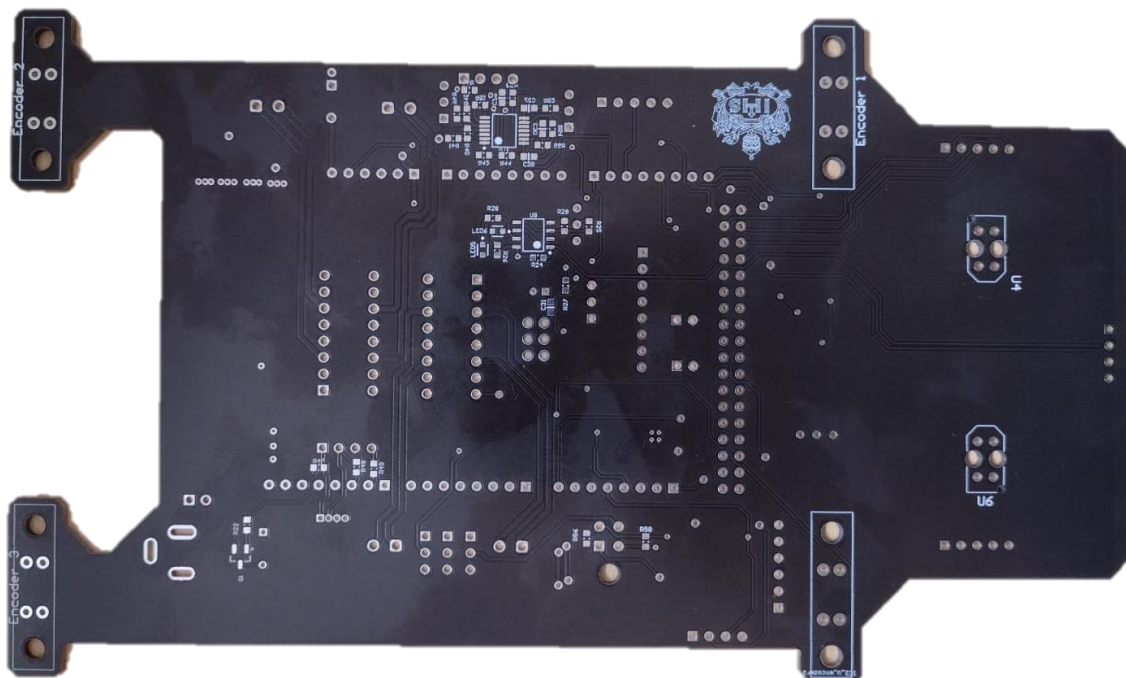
Vista inferior del PCB fabricado versión 3 (Final)
